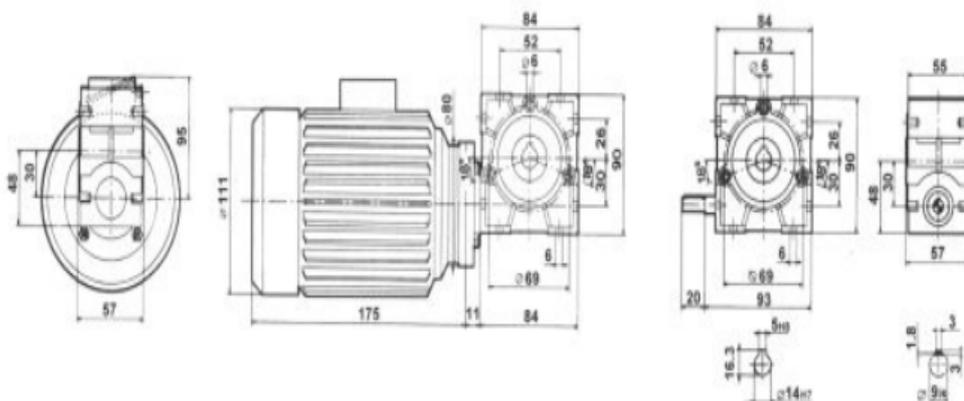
Dimensiones del reductor para calibración de grosor de paso del cuero
